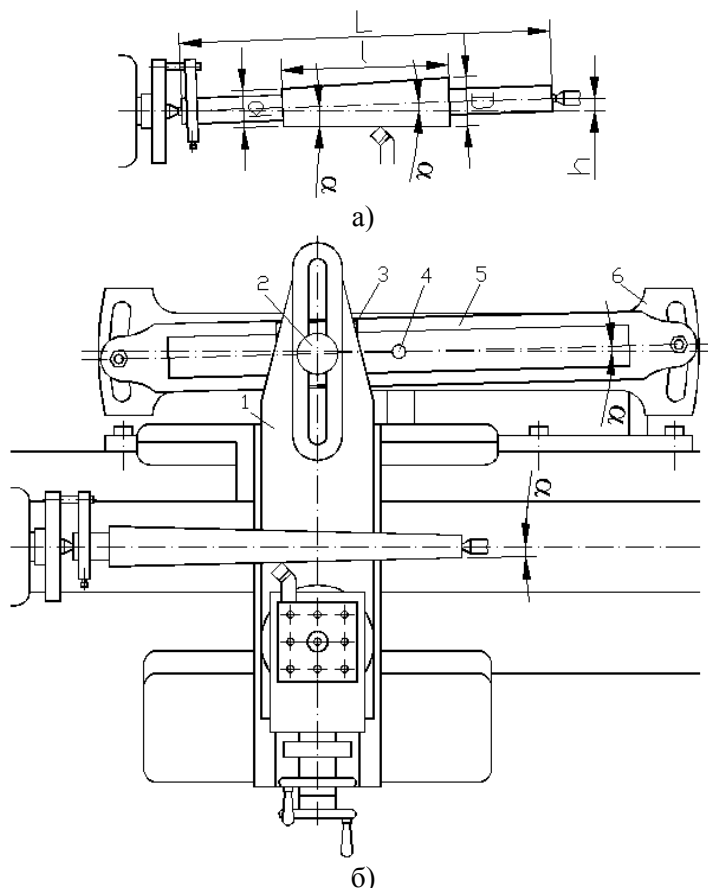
Способы обработки конических поверхностей на токарном станке:
